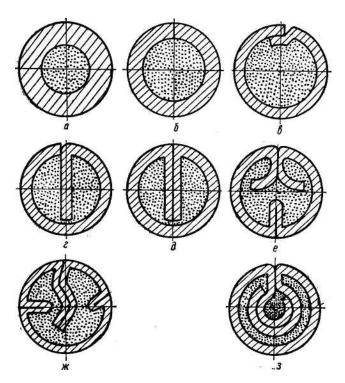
Виды порошковой проволоки по форме сердечника
